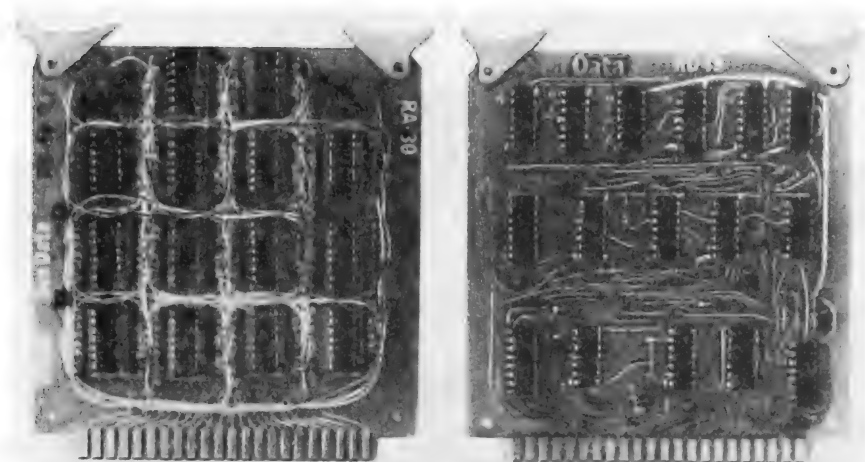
Плата-прототип с контактами накруткой и печатная схема – ее преемник. В печатной плате отсутствуют перекрестные помехи, и она гораздо проще для изготовления большими партиями. Кроме того, в ней исключены ошибки при монтаже проводов.
